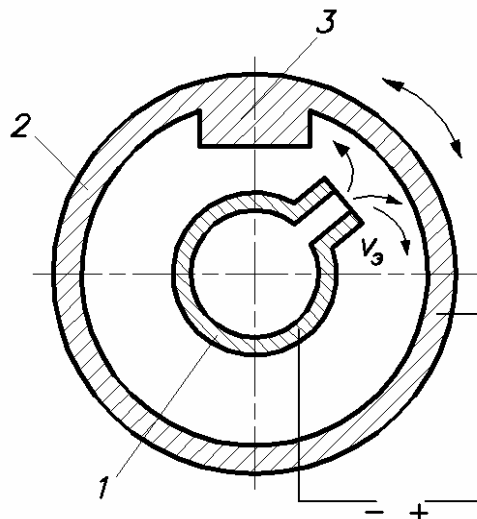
Схема точения при обработке части нежесткой заготовки:
